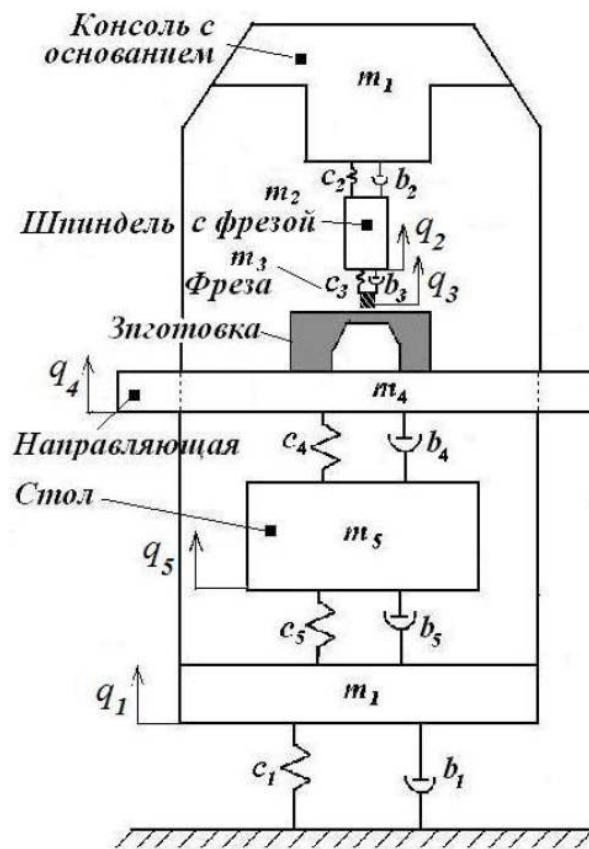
Динамічна модель типового вертикально-фрезерного верстату 6Р13 [45]
